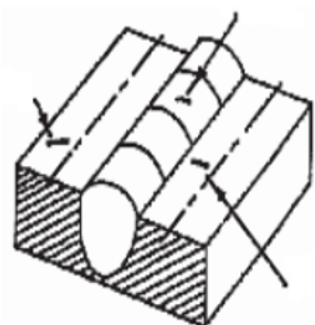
Эскиз дефекта сварного шва
